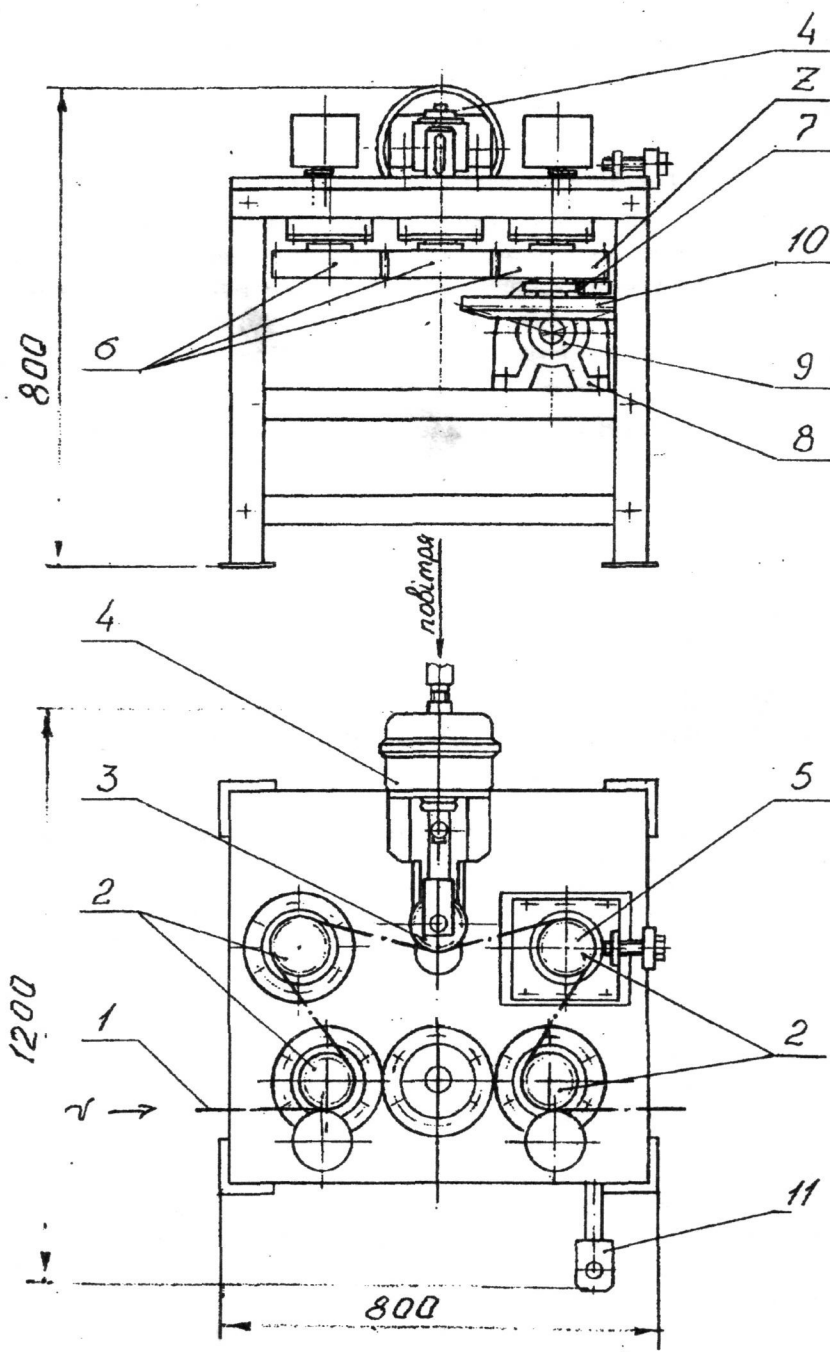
Конструктивна схема верстата для пластичного деформування приводних ланцюгів
